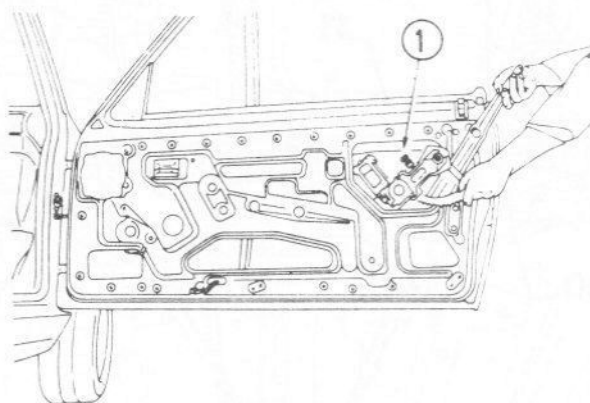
Vis de réglage de hauteur de glace de porte (1) – illustrée au cours de la dépose du lève-glace – modèles Cabriolet (Sec 21)
